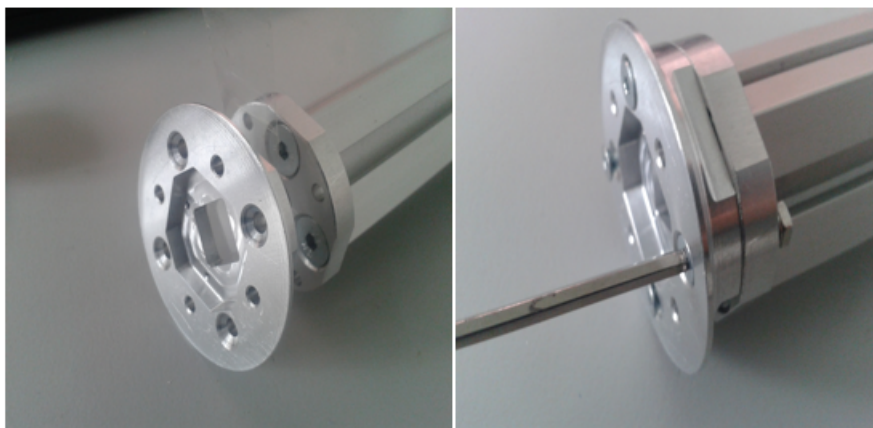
A11 conical flange plate mod für Boschprofil
